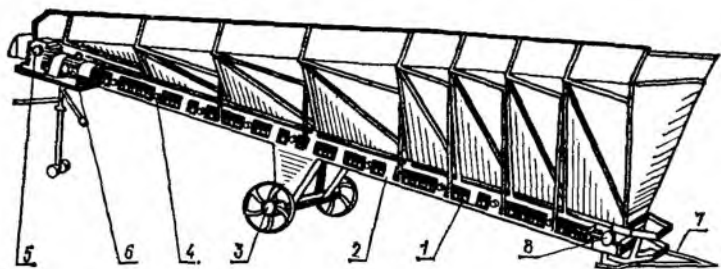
Приемный бункер ПБ-4 конструкции ГСКБ (г. Рязань): 1 — полотно; 2 — рама; 3 — колесо; 4 — поддерживающий барабан; 5 — ведущий вал; 6 — привод; 7 — прицел; 8 — ведомый вал.
